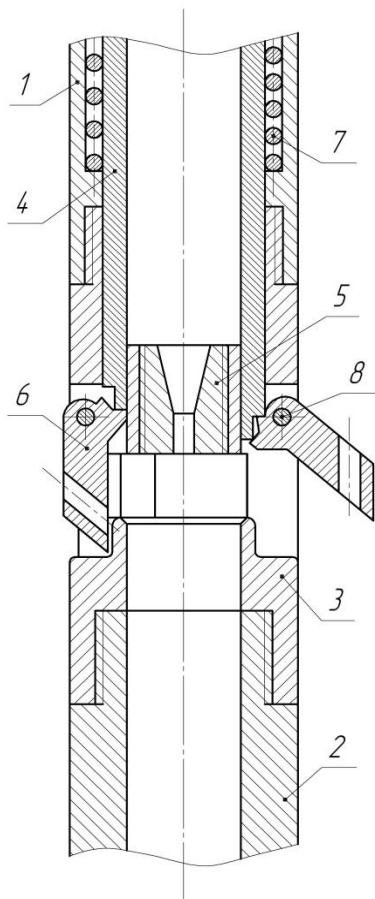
ЗУ со складывающимися лепестками рычажного типа:
